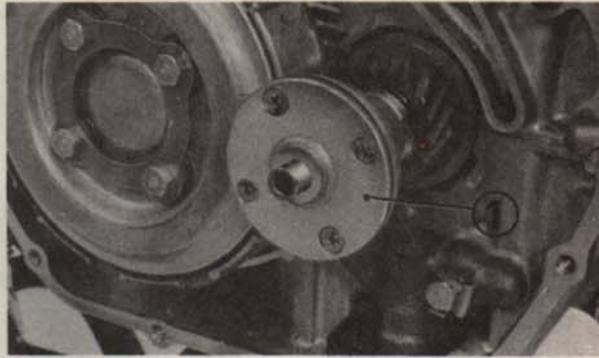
(1) Couvercle de protection de rotor de filtre à huile
